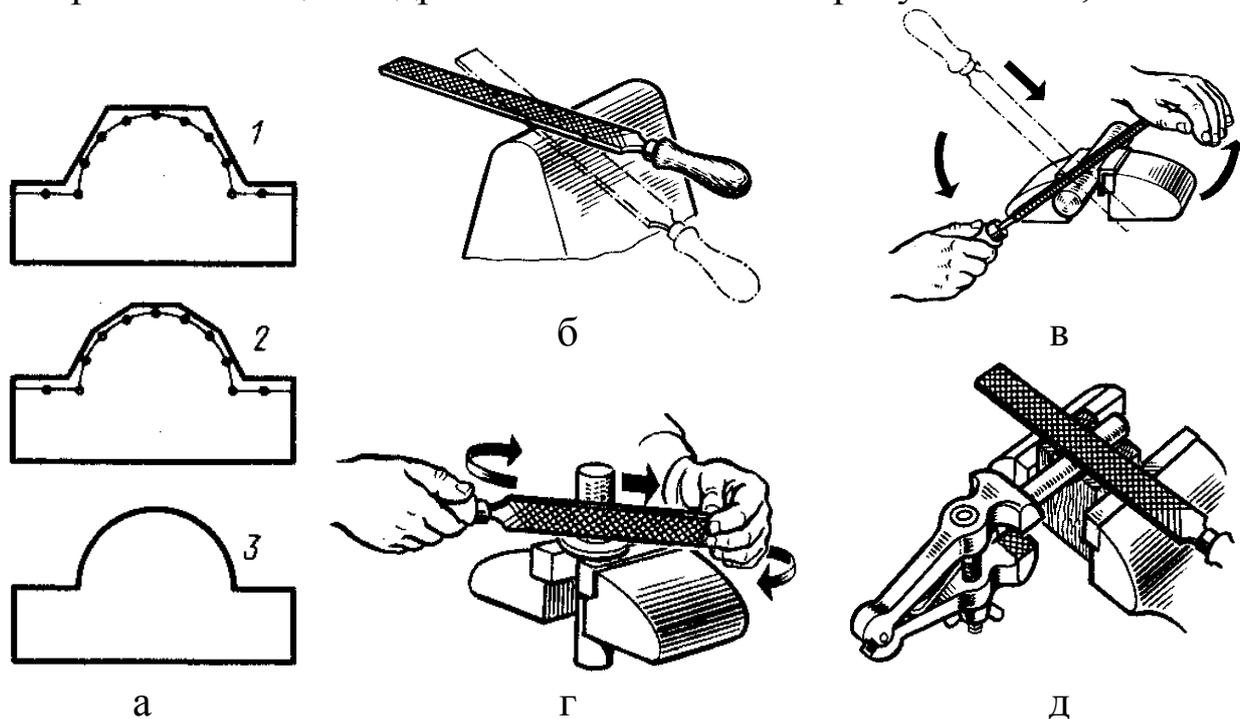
Приемы опилования наружных криволинейных поверхностей: а - последовательность обработки: 1 - срезание излишнего металла; 2 - опилование черновое; 3 - опилование чистовое; б - опилование выпуклой поверхности; в - опилование стержня, закрепленного горизонтально; г - опилование стержня, закрепленного вертикально; д - опилование цилиндрического стержня, закрепленного в ручных тисках
